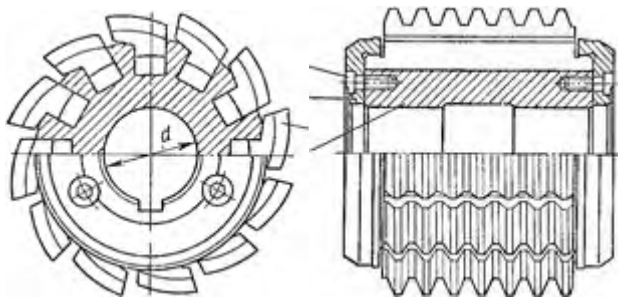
Черв'ячна фреза з поворотними вставними рейками
